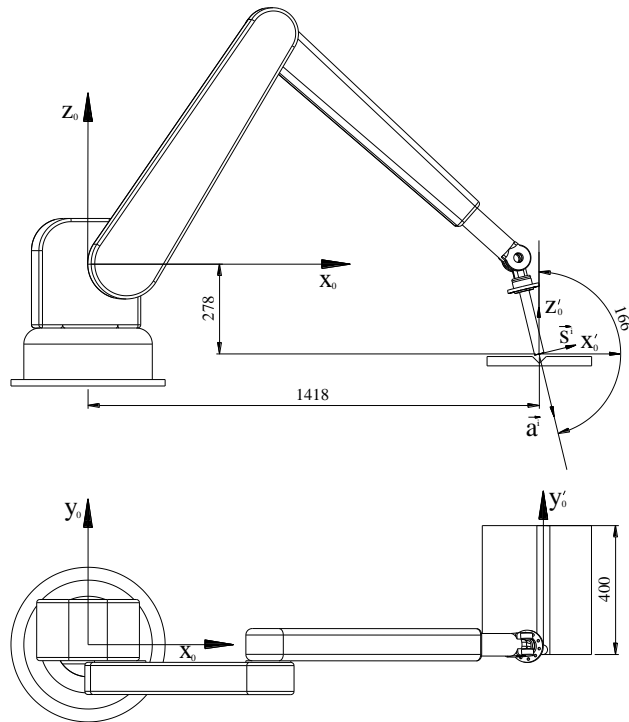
Soudage de deux tôles (bout à bout) par un robot de 6 axes
